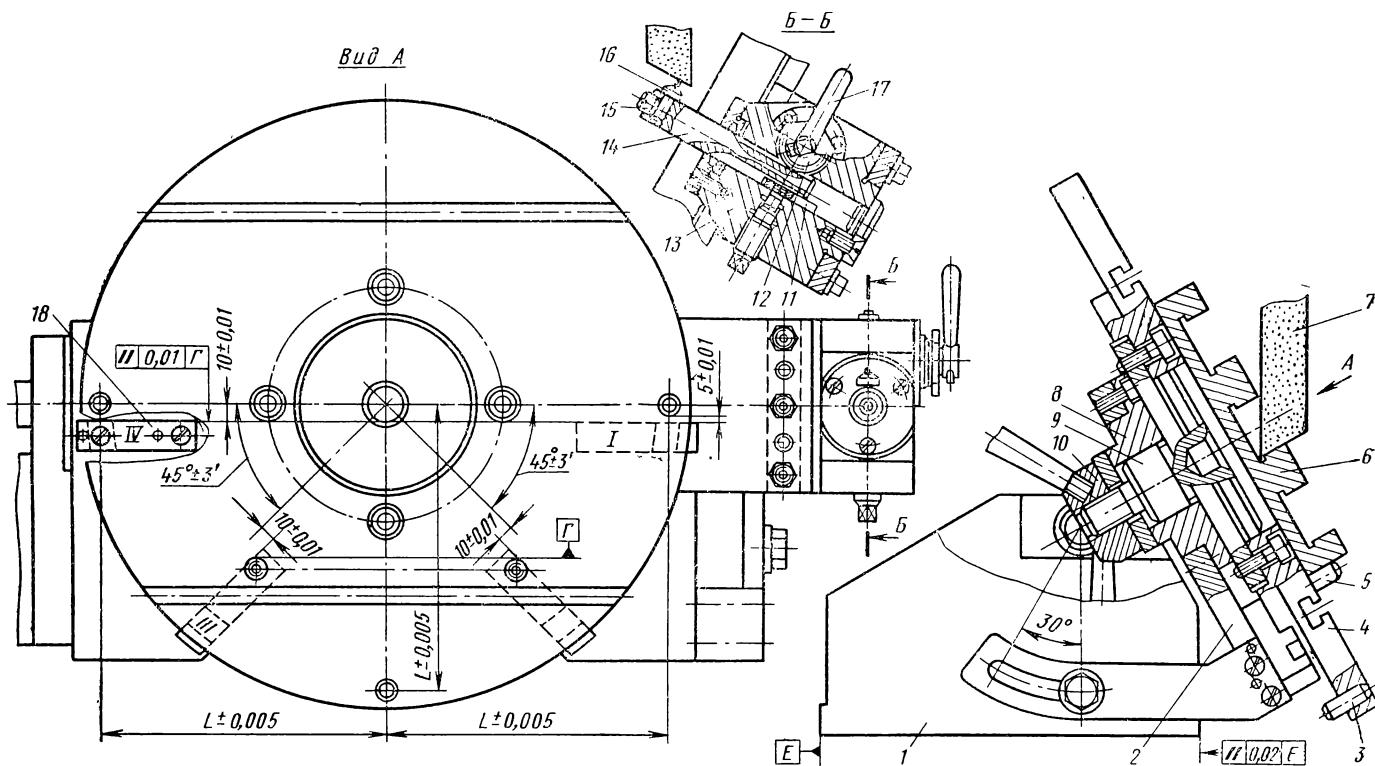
Приспособление с поворотным столом для шлифования пазов
